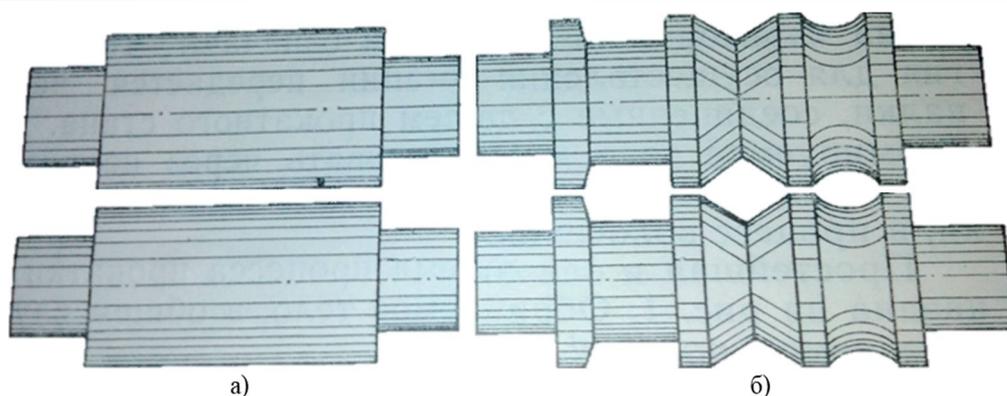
Основные прокатные валки с гладкой бочкой (а) и калиброванные валки (б), используемые в металлургическом комбинате республики
